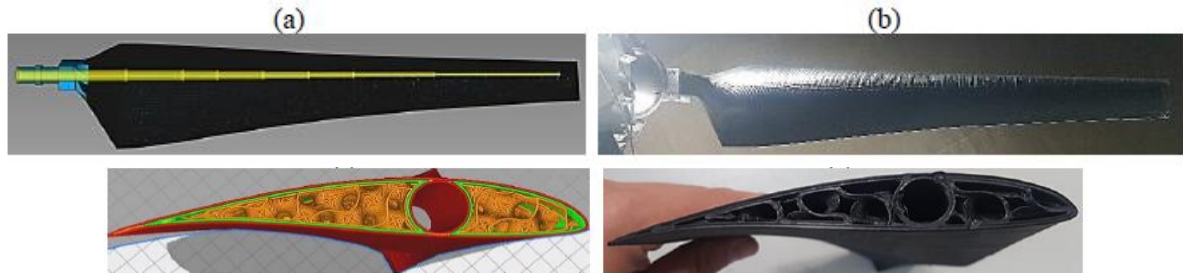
a) Diseño de rotor con el larguero incrustado en el alabe. b) Alabe impresa en 3D durante pruebas en el túnel de viento; c) Sección transversal alabe en Diseño. d) Sección transversal alabe fabricada.
